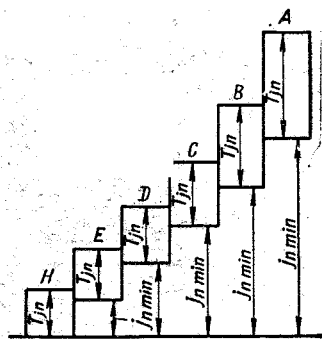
Схема наименьших значений бокового зазора и допусков зазоров
